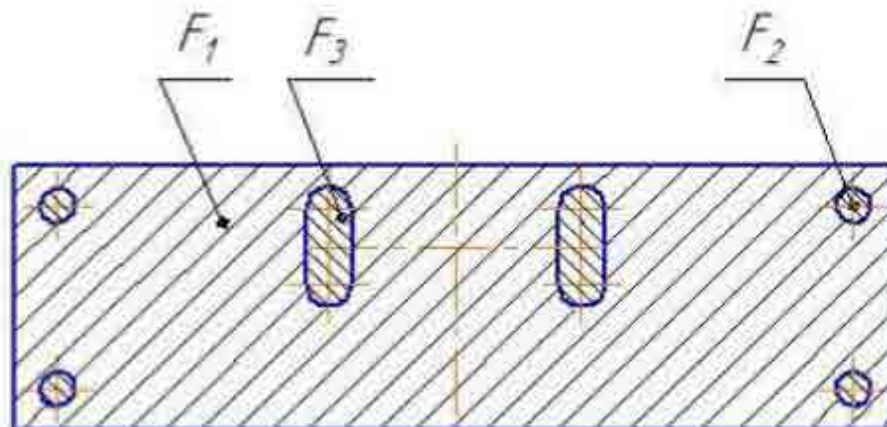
До розрахунку площі поверхні заготовки
